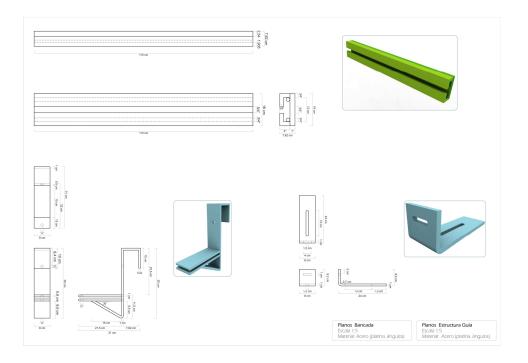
Planos Palancas de Fijación de Desplazamiento de la Guía
